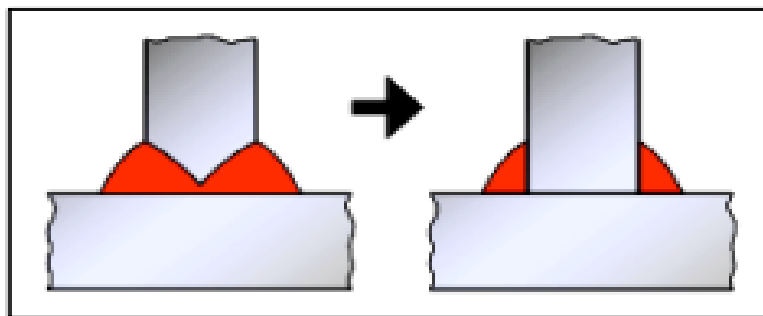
a : Configuration du Joint la soudure à deux angles
